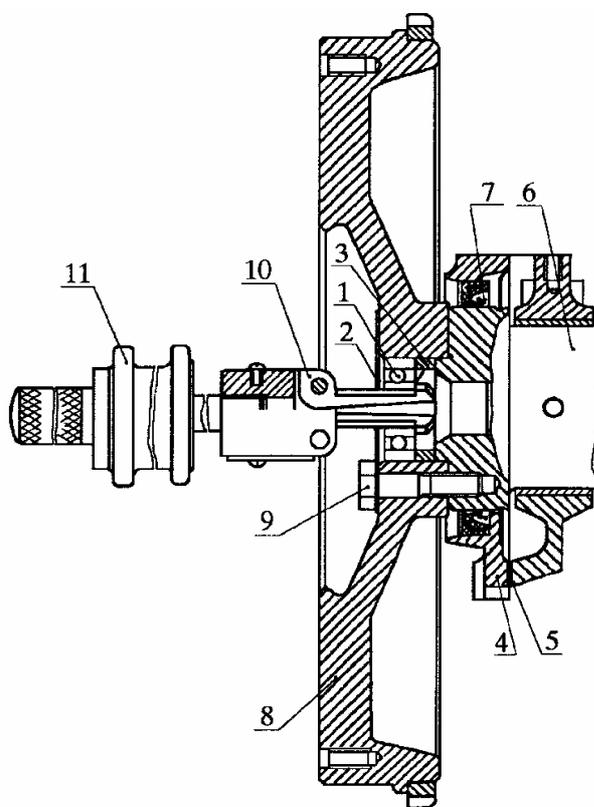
Снятие подшипника первичного вала коробки передач:
